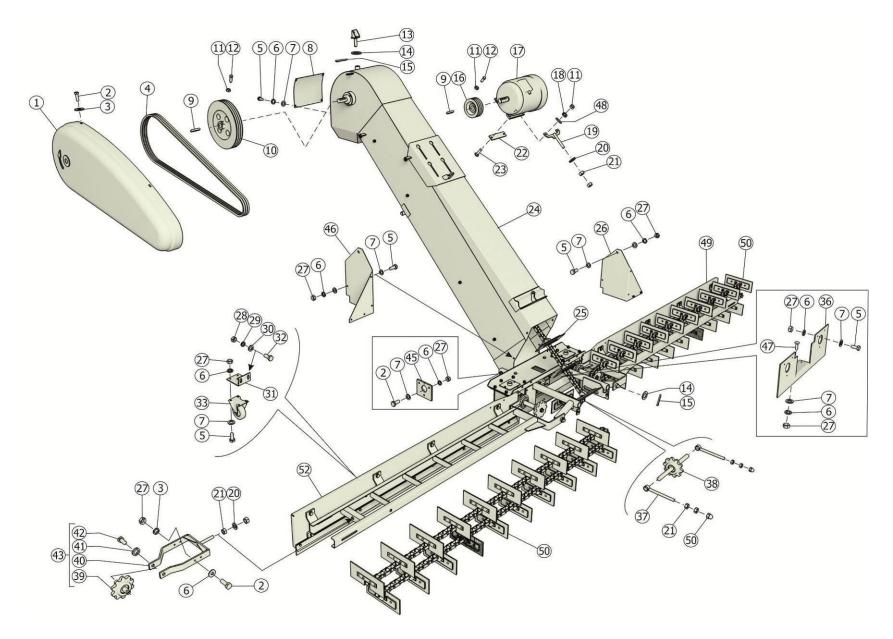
Транспортер загрузочный M3C-90.23.000 87
